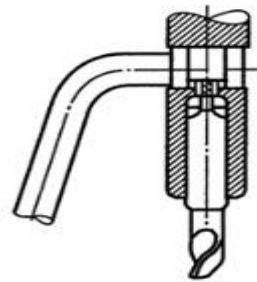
Эксцентриковый ключ для удаления режущего инструмента из шпинделя станка
